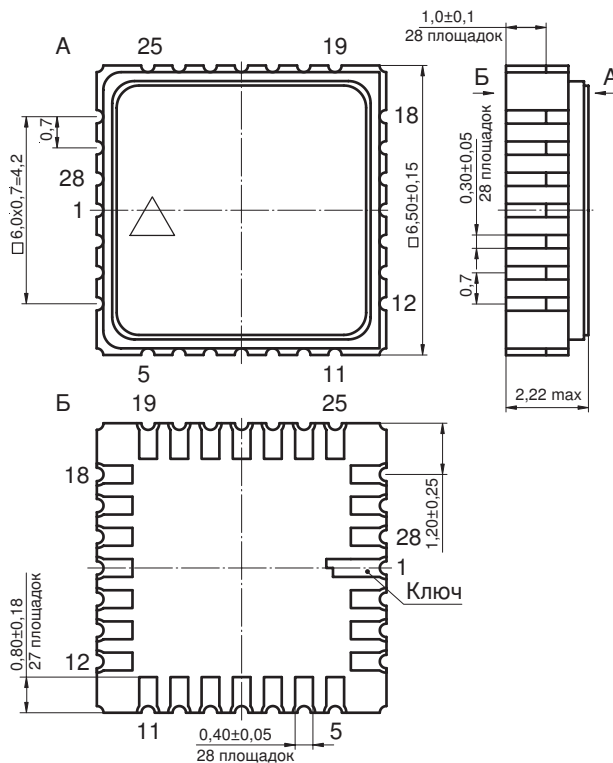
Чертеж корпуса МК 5123.28-1.01
